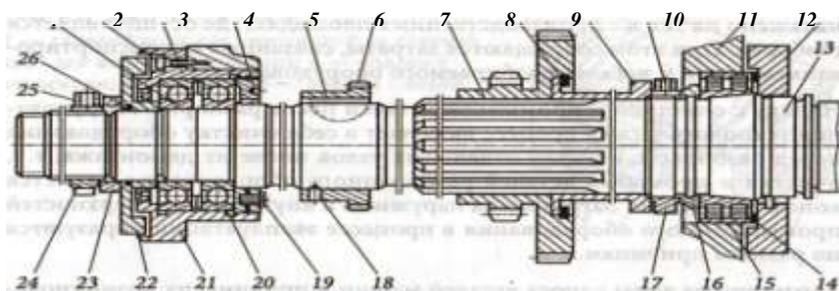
Шпиндельный узел токарного станка мод. 16К20:
